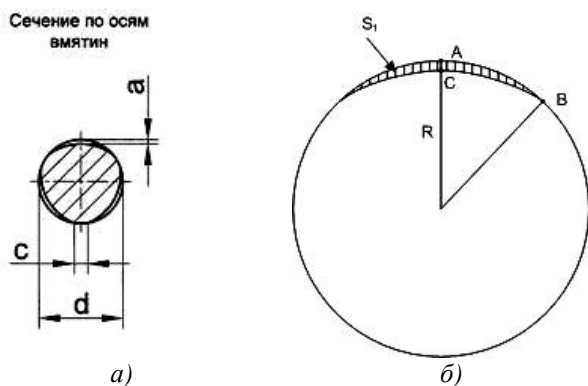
Площадь поперечного сечения прутка: а – основные размеры, определяющие качество нанесения профиля, б – к определению площади поперечного сечения
